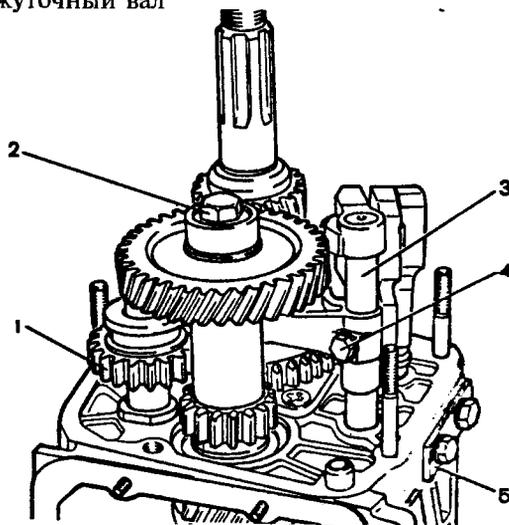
Отвертывание болтов крепления блока шестерен и вилок включения V передачи и заднего хода: 1 - промежуточная шестерня заднего хода; 2 - болт крепления блока шестерен; 3 - шток вилки; 4 - болт крепления вилки; 5 - крышка фиксаторов
